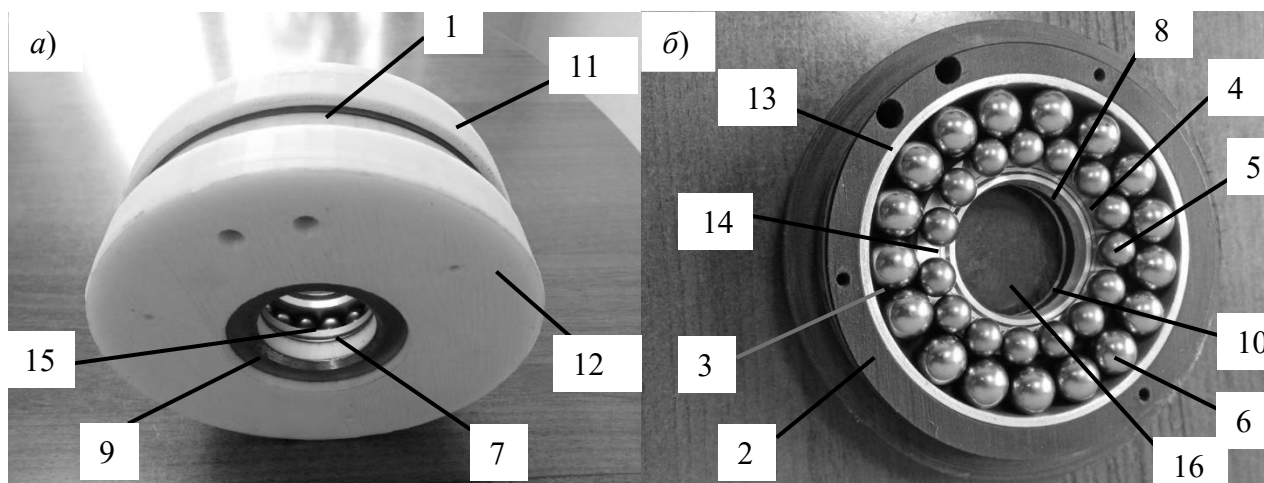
Конструкция инструмента для совмещенного магнитно-динамического накатывания поверхностей валов: *а* – вид инструмента; *б* – обойма инструмента с расположенными в нем деформирующими шарами и отражателями
